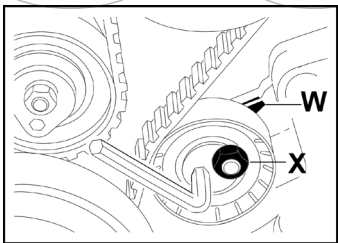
Agendo sul tenditore T3, portare l'indicatore mobile W nella posizione di tensione, serrare quindi il dado di fissaggio X.
